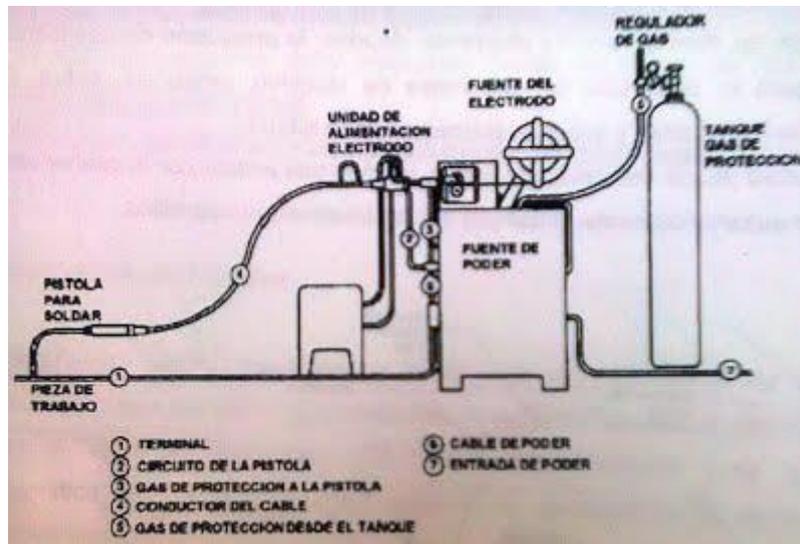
Equipo de soldadura por arco de metal y gas (GMAW). Recuperado de: (Hernández Cano, 2013)
